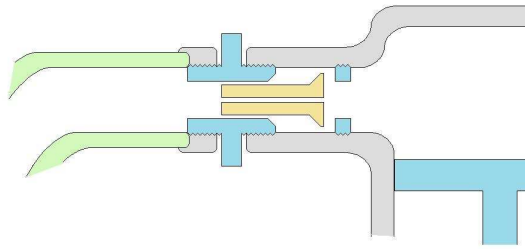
Dessin en coupe des pièces utiliser dans le système.
